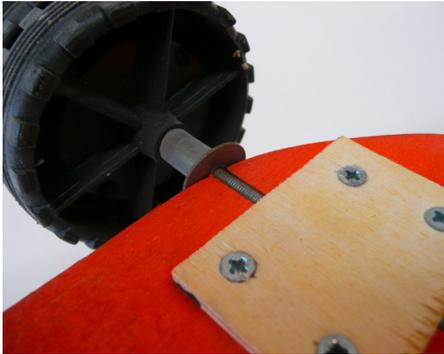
| Achse im genuteten Brett und Abstandhalter durch einen Kunststoffrohrabschnitt
